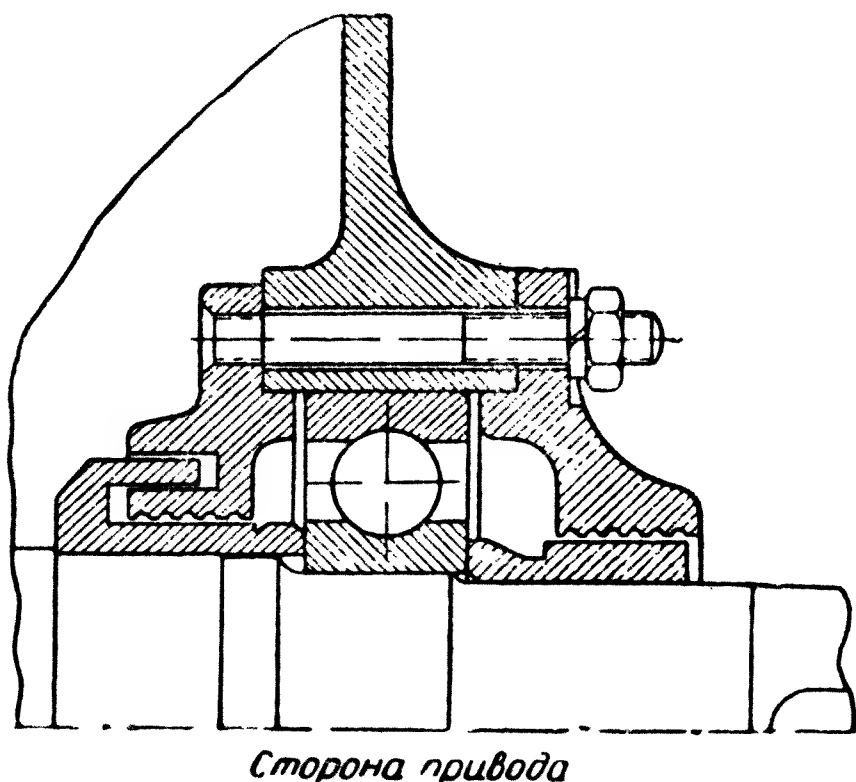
Подшипниковый узел с шарикоподшипником.
